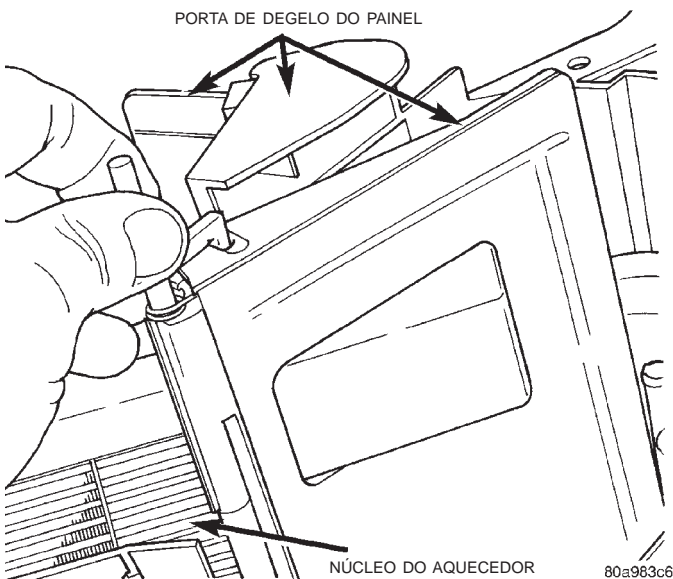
Remoção/Instalação da Porta de Degelo do Painel
